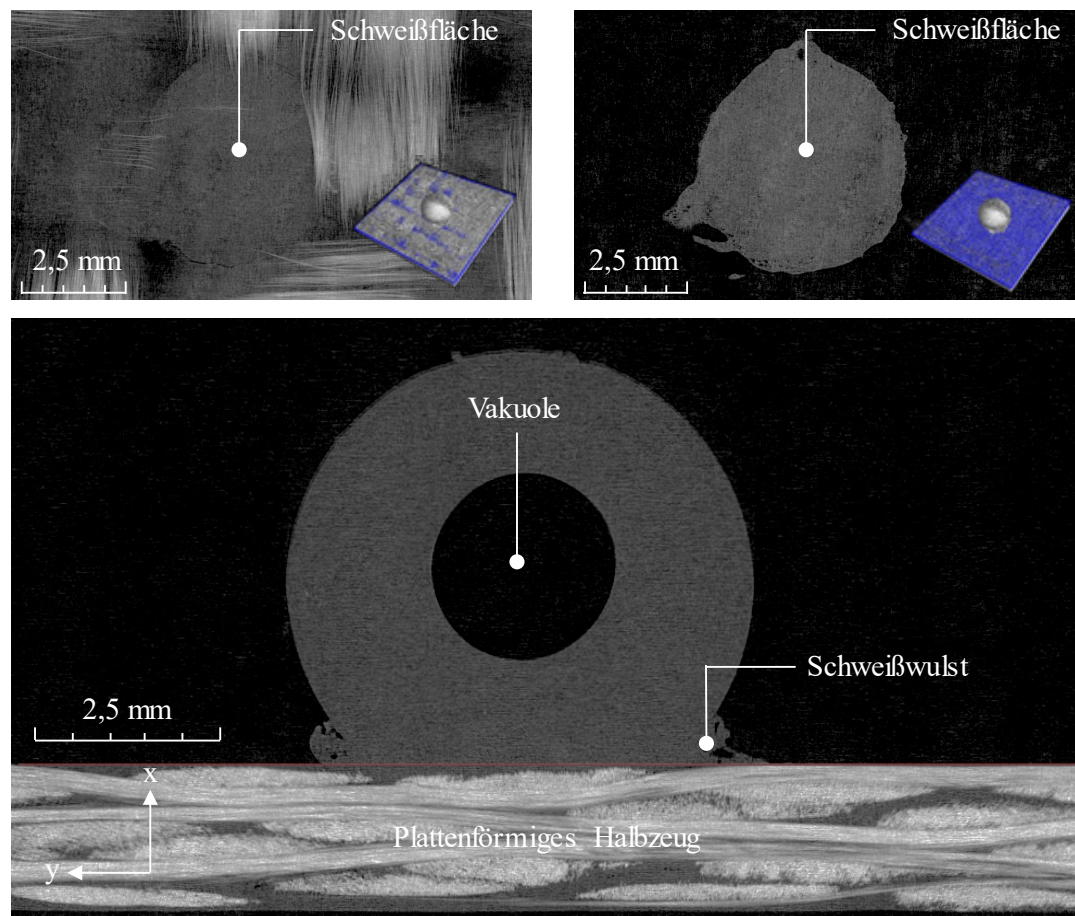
CT-Bild der Schweißverbindung PP-GF/PP [138]
